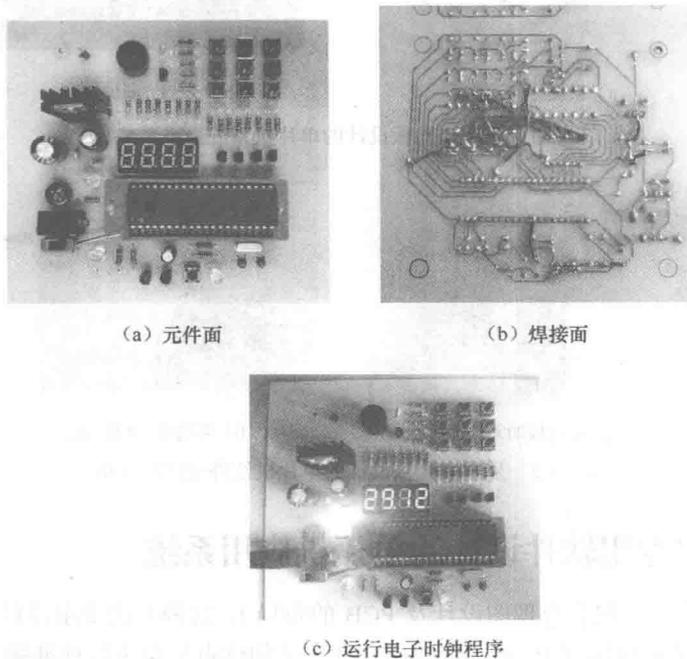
由大学生自己制作的单片最小系统 PCB 板
